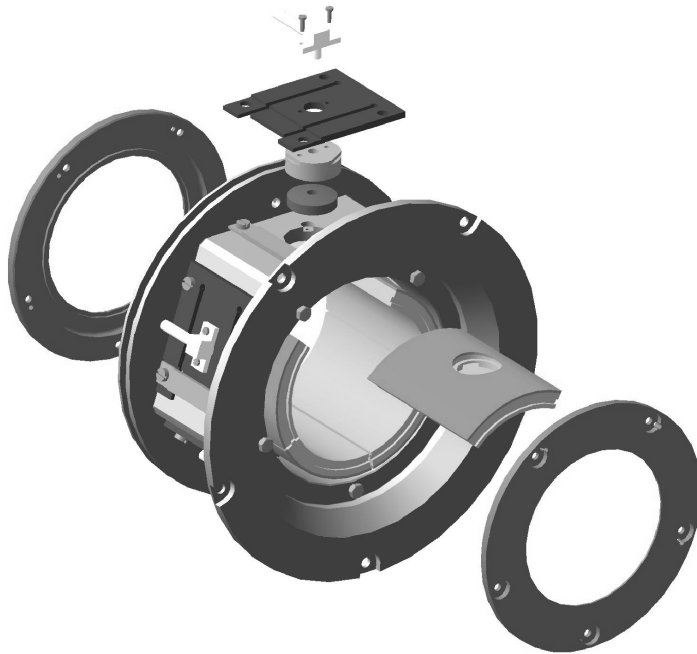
Конструктивная схема подшипника с самоустанавливающимися сегментными вкладышами
